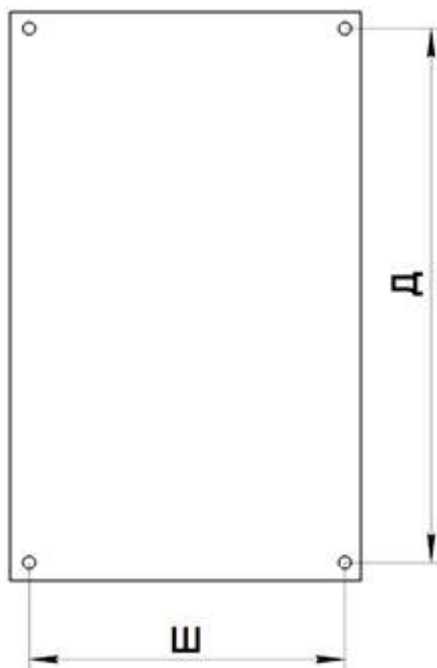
установочные размеры ПУ-4-X Y Z
